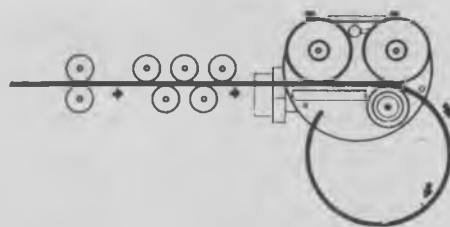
Схема работы протяжного механизма при изготовлении спиралей
